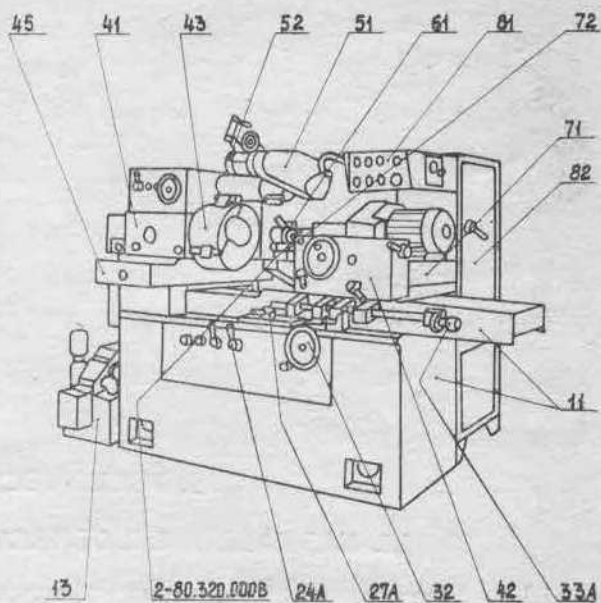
Общий вид станка мод. 3К227В с обозначением узлов.
